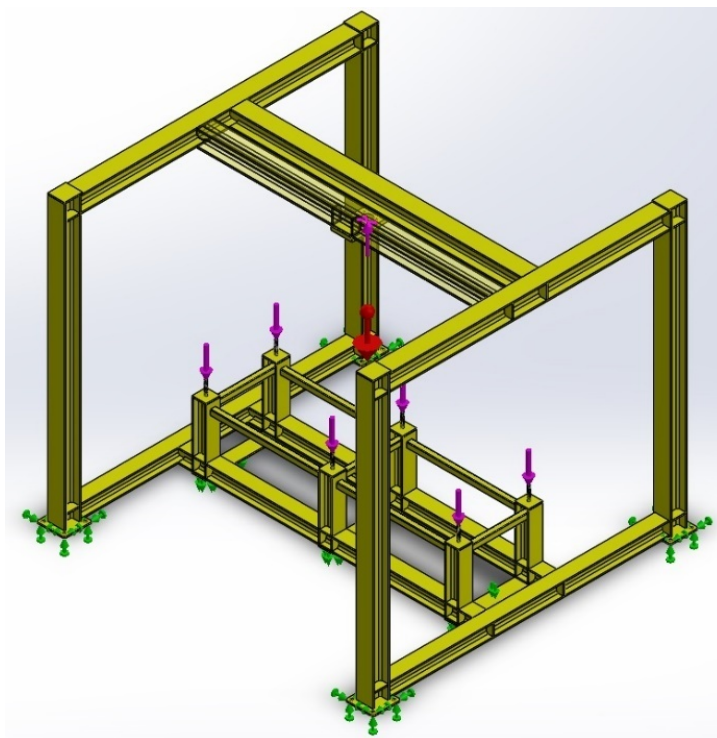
Detalle de aplicación de cargas en la estructura principal
